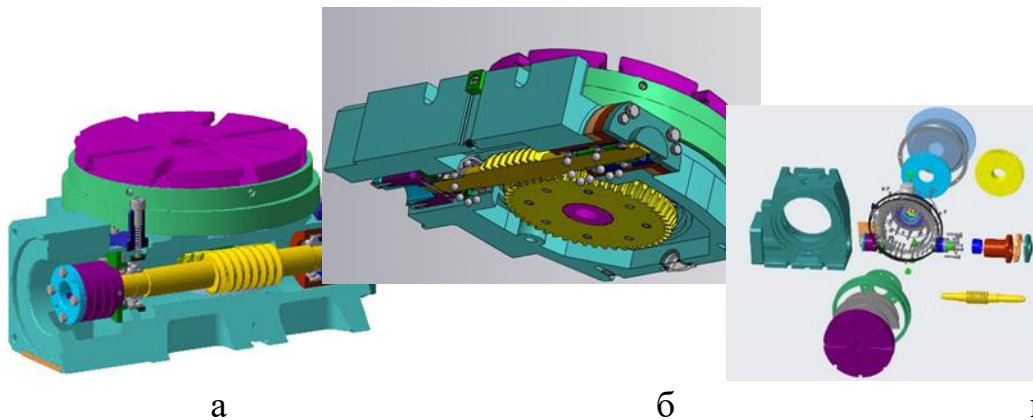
3D моделювання поворотного столу: а; б – переріз; в – рознесення
